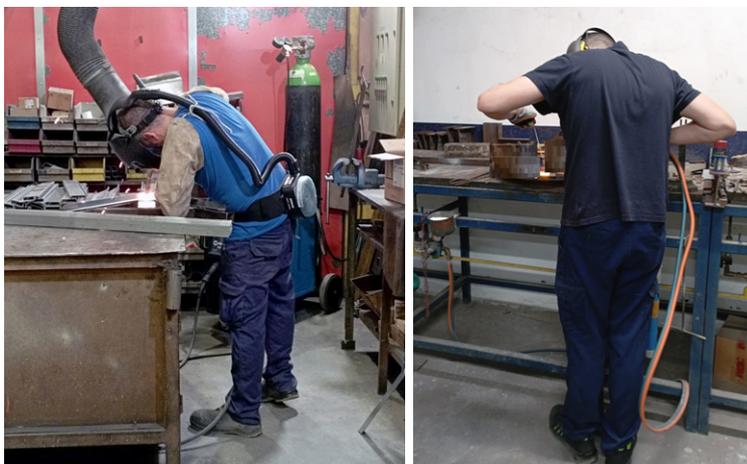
Diferentes posturas adoptadas durante trabajos de soldadura.
